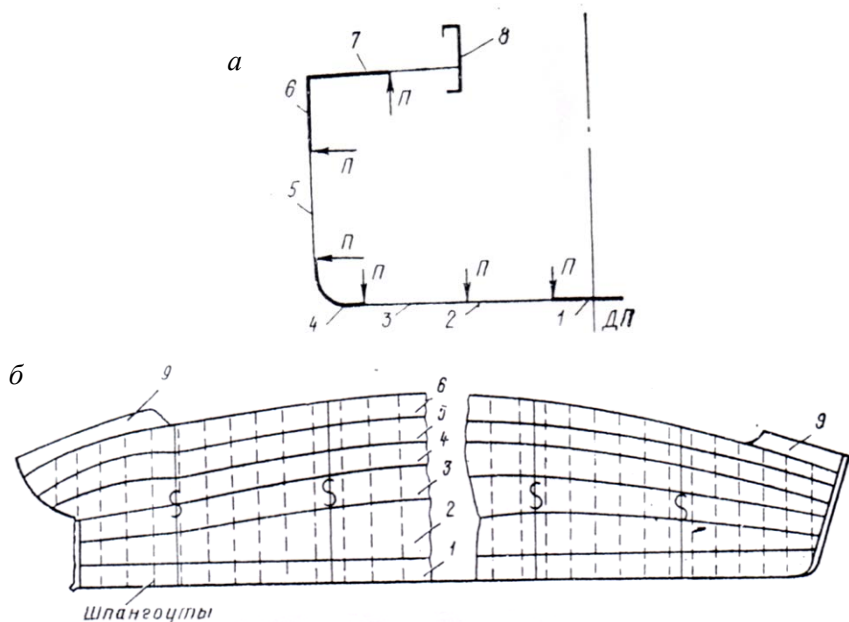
Обшивка корпуса в поперечном сечении (а) и растяжка наружной обшивки (б):
